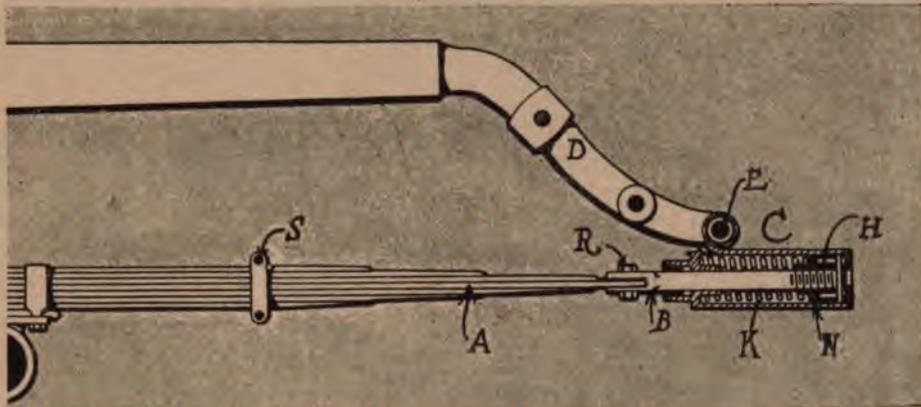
Stoßdämpfer, welcher gleichzeitig zur Aufhängung des hinteren Federendes dient; A Feder; B Kolbenstange; C Zylinder; D Federträger; E Gelenk; H Kolben; K Spiralfeder; N Dichtung des Kolbens; R Gelenkbolzen; S Federklammer.
